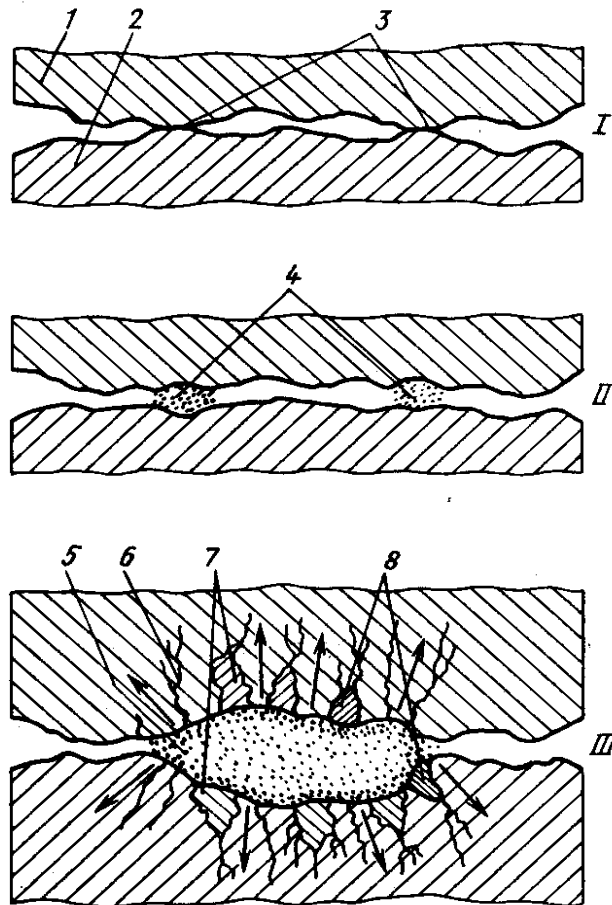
Механізм зношування металевих поверхонь при фретинг-корозії:
